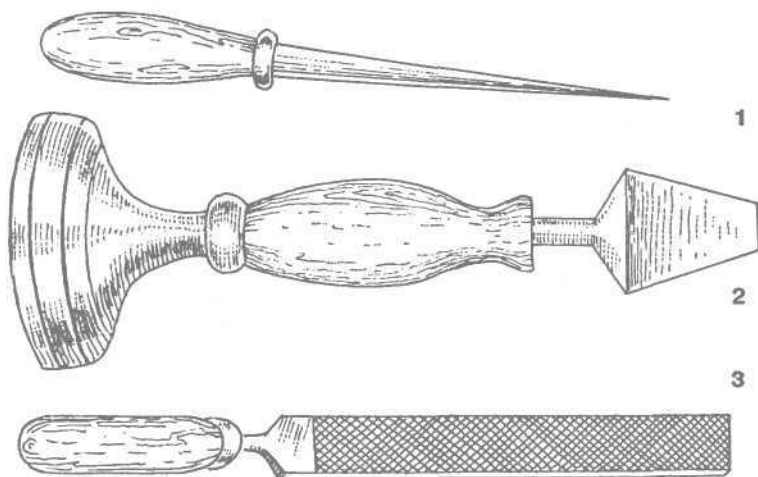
Формовочный инструмент: 1 — вентиляционная игла; 2 — трамбовка формовочная; 3 — правильный брусок
